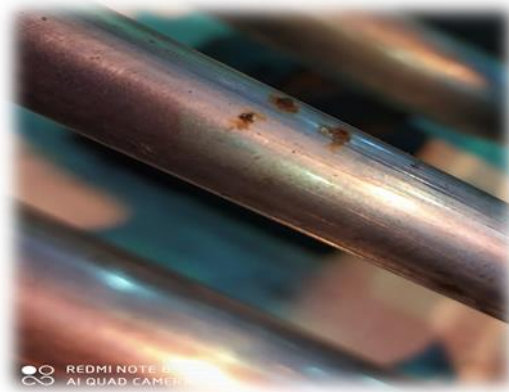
Grain de soudure déposé sur le tube d'huile hydraulique
